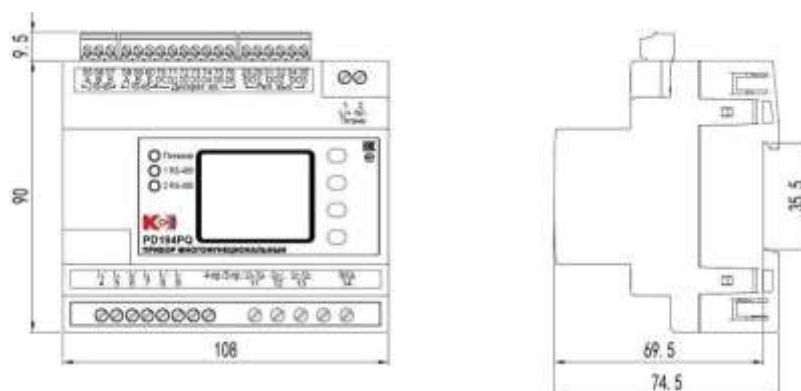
Внешний вид и размеры прибора PD194PQ-7B3T-11001
